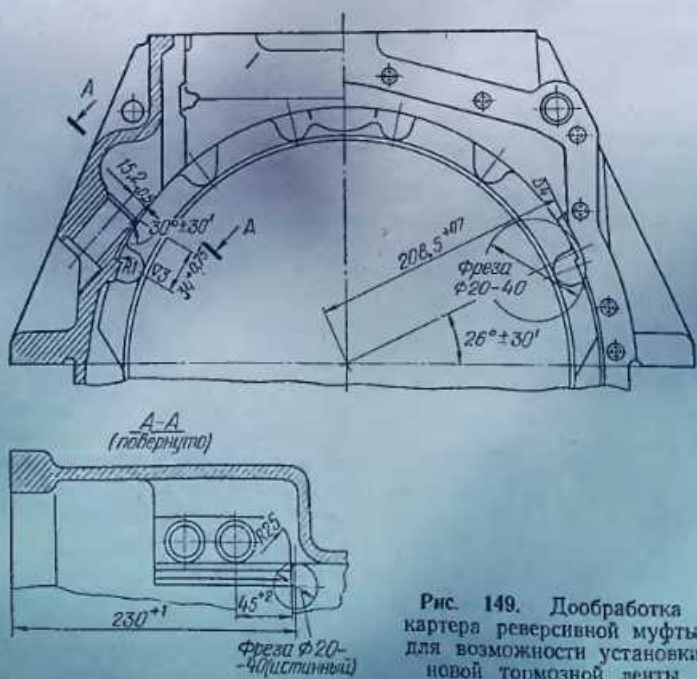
Дообработка картера реверсивной муфты для возможности установки новой тормозной ленты
